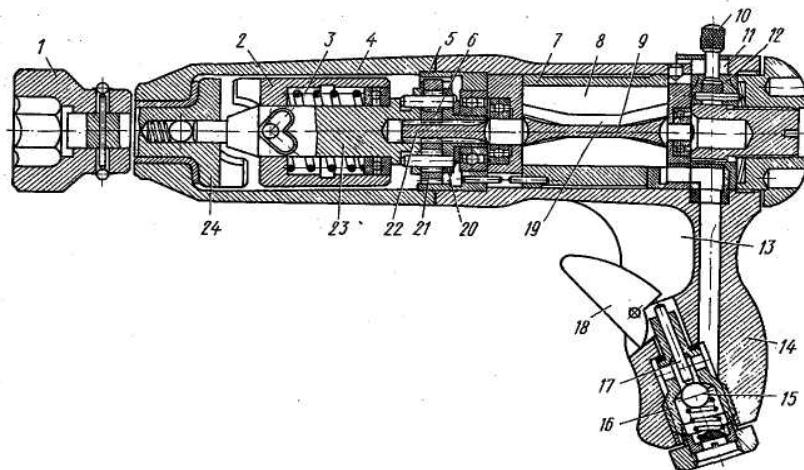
Пневматический реверсивный гайковерт ИП3102
